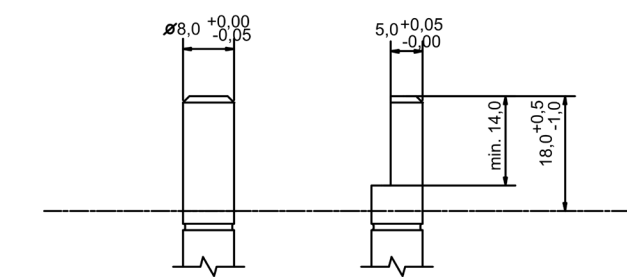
Seitenansicht, Geberwelle/Side view, encoder shaft/Vue latérale, arbre du codeur
